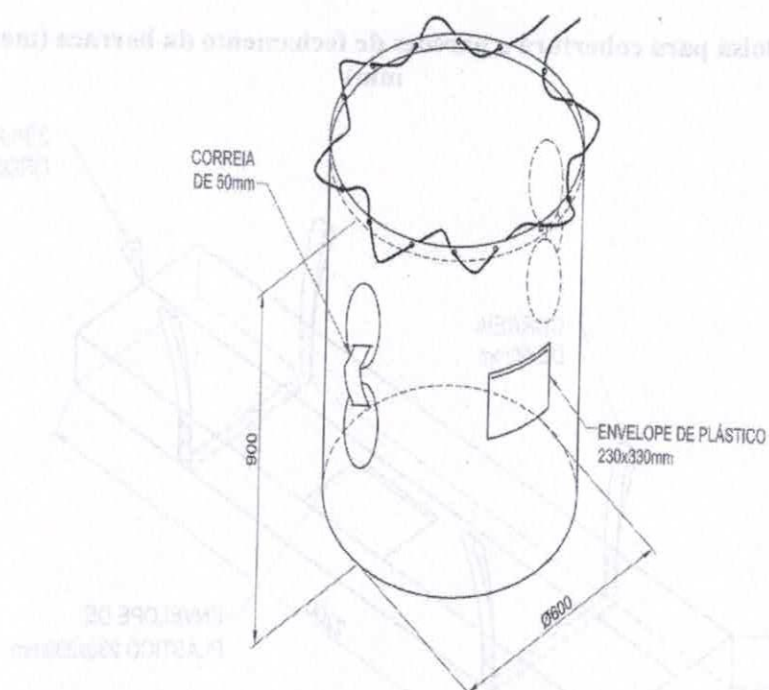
Bolsa para do forro térmico da barraca (medidas em mm)
